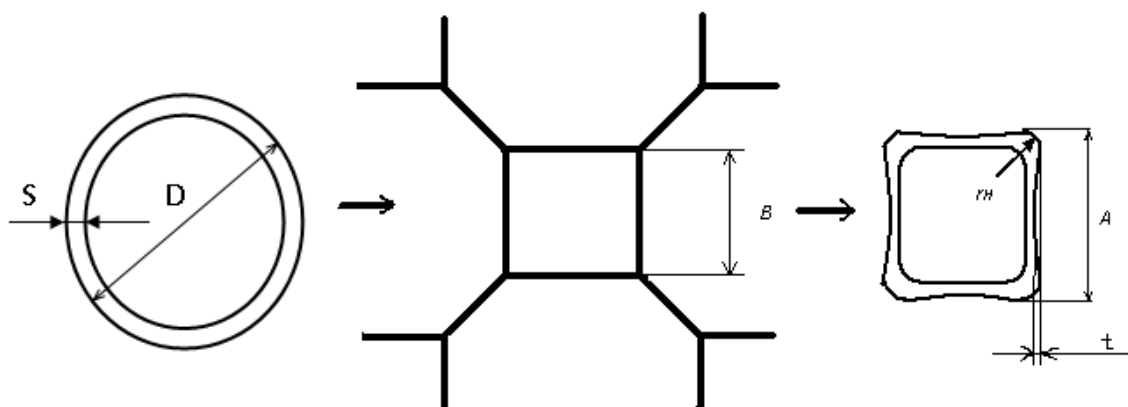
Схема профилирования и геометрические параметры сечения исходной заготовки и готового профиля
